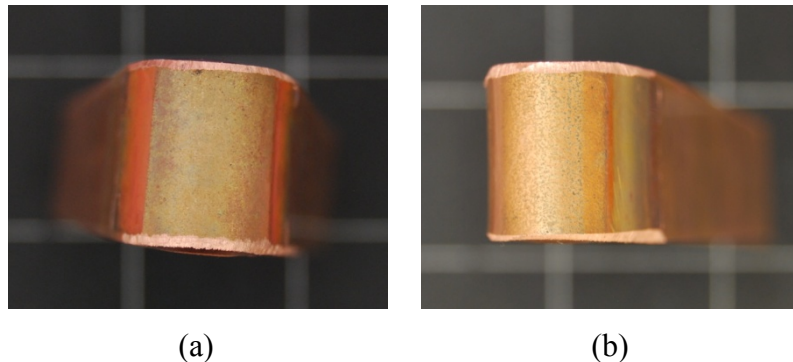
Comportamento à dobragem das soldaduras: (a) *CuW10V10*; (b) *CuW12.5V40*.
